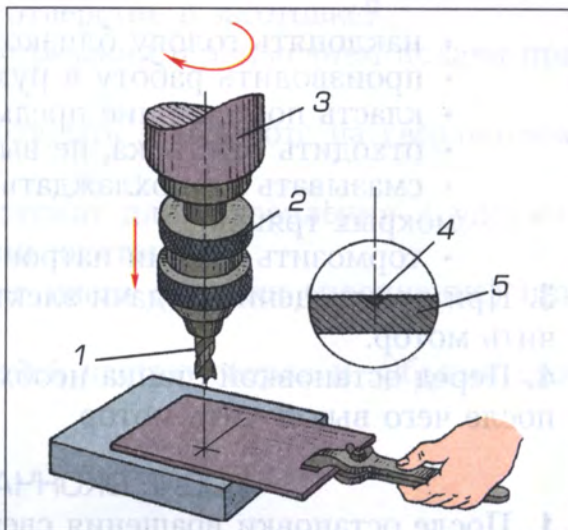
Сверление: 1 – сверло, 2 – патрон, 3 – шпиндель, 4 – керн, 5 – заготовка
